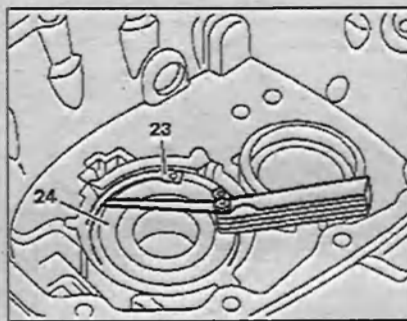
Регулировка зазора подшипника вторичного вала.
